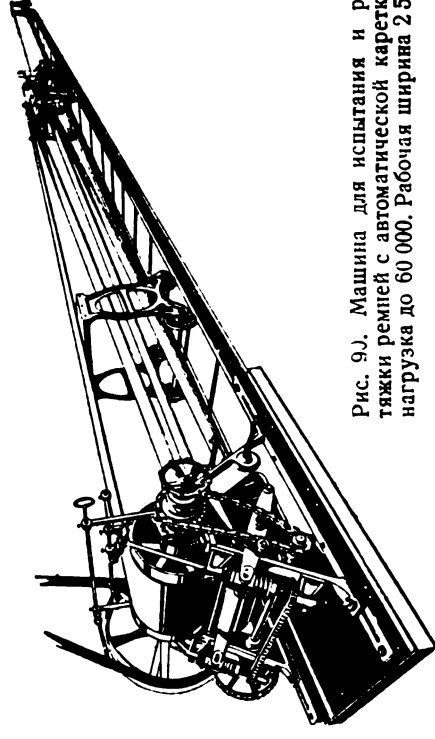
Машина для испытания и растяжки ремней с автоматической кареткой, нагрузка до 60 000. Рабочая ширина 2500.
